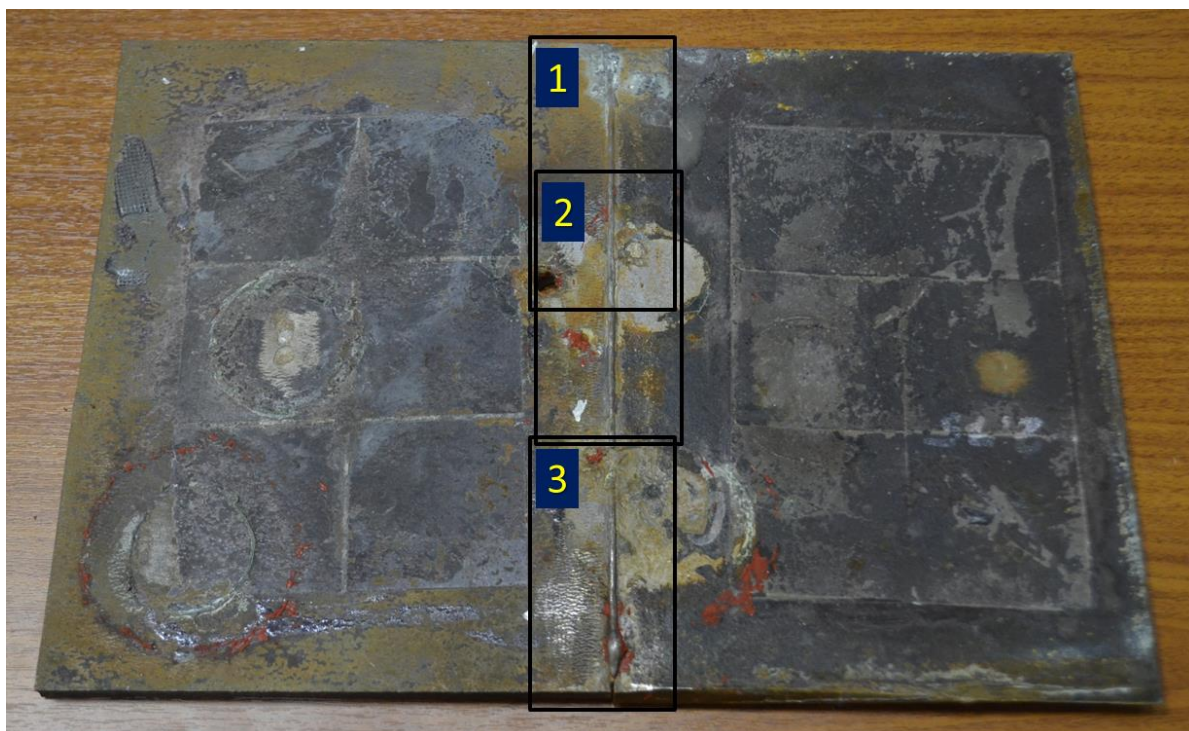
Зоны сканирования сварного шва броневой пластины
